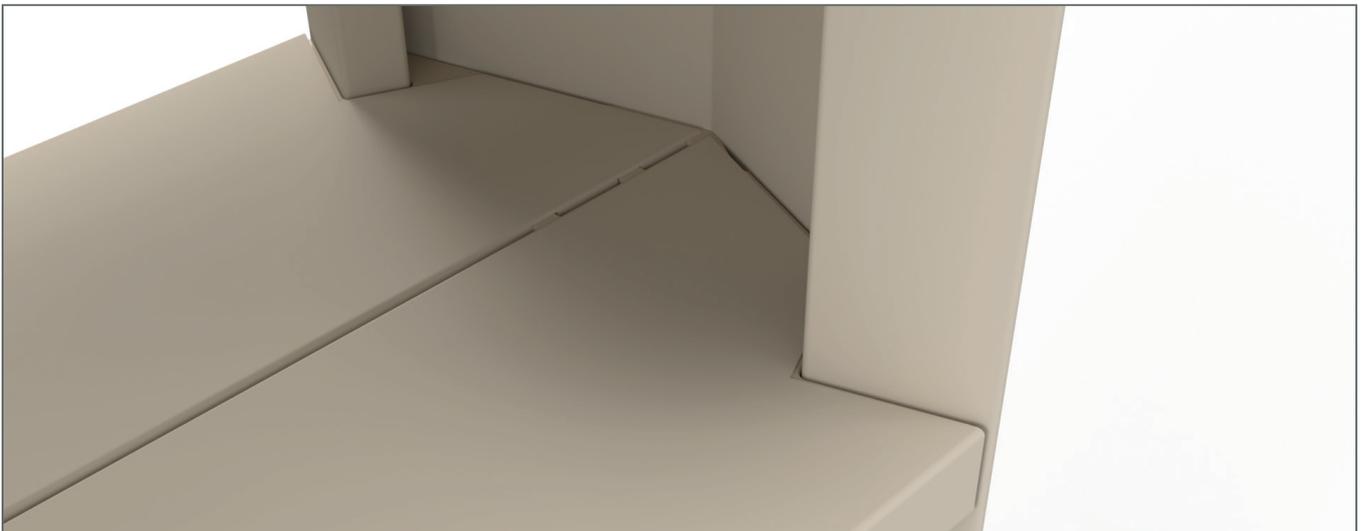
Rendering Regal Detail 2. Detaillierte Ansicht auf Fachbodenverbindungsstelle.
